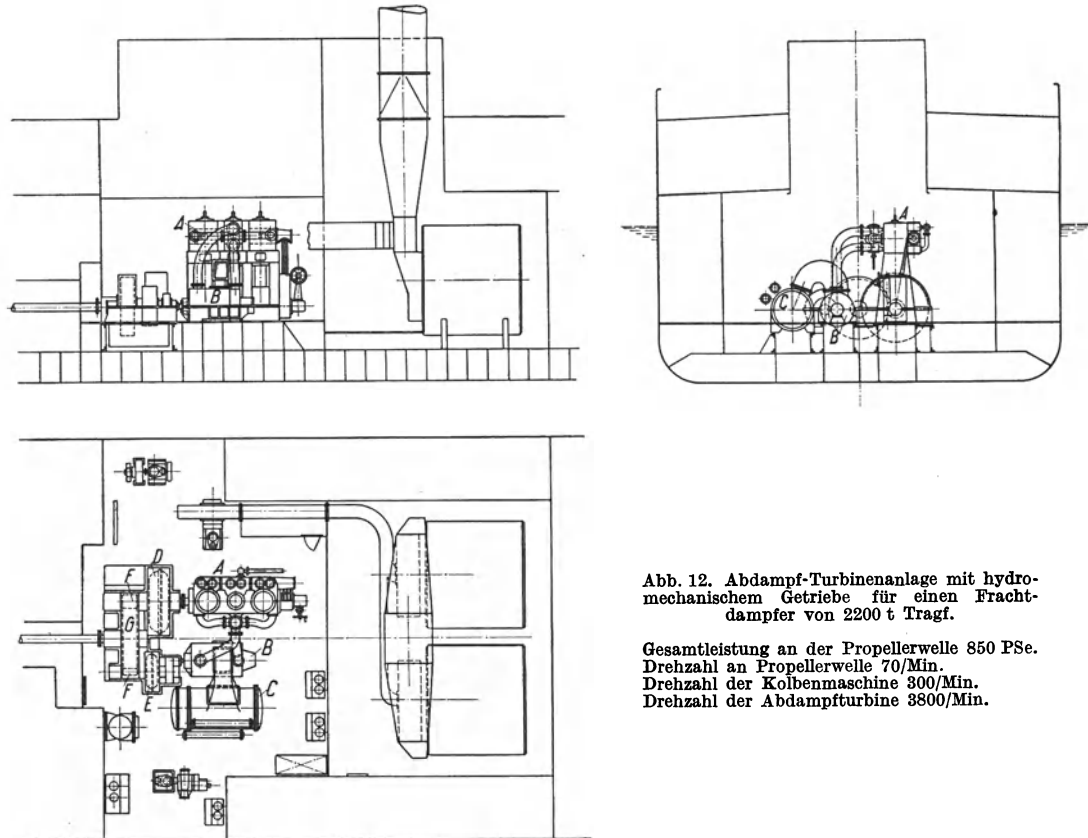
Abdampf-Turbinenanlage mit hydro-mechanischem Getriebe für einen Frachtdampfer von 2200 t Tragf.
